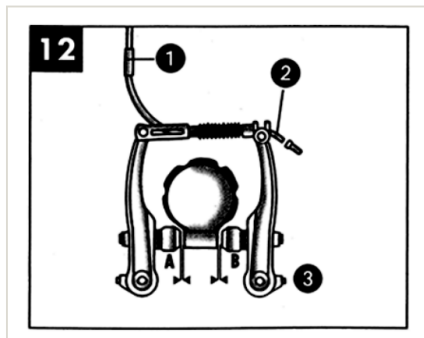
1 tube aluminium · 2 couple de serrage 6/8 Nm · 3 A + B = 3 mm
